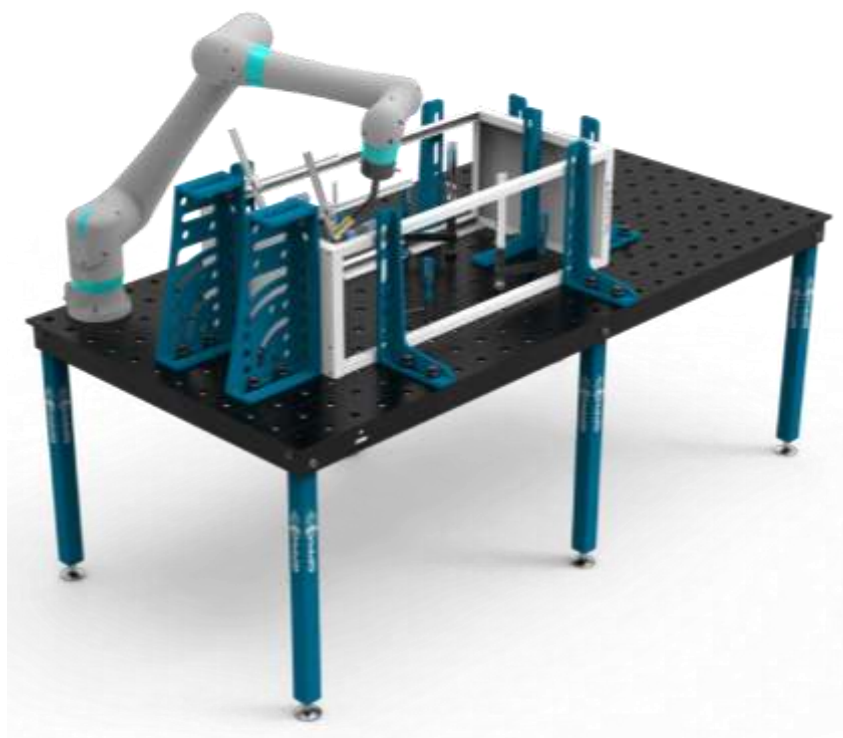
Приклад використання зварювального стола зі зварювальним роботом
